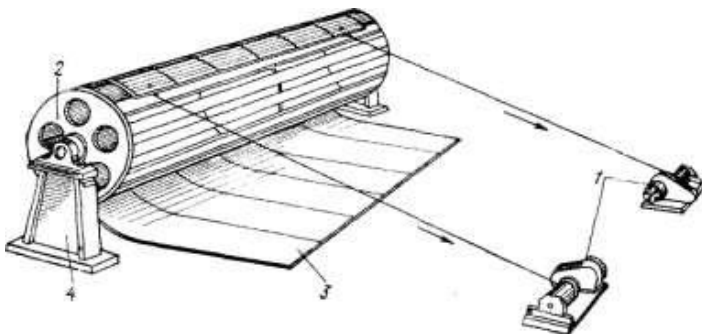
Поворотное приспособление для кантовки полотнищ на 180°:
